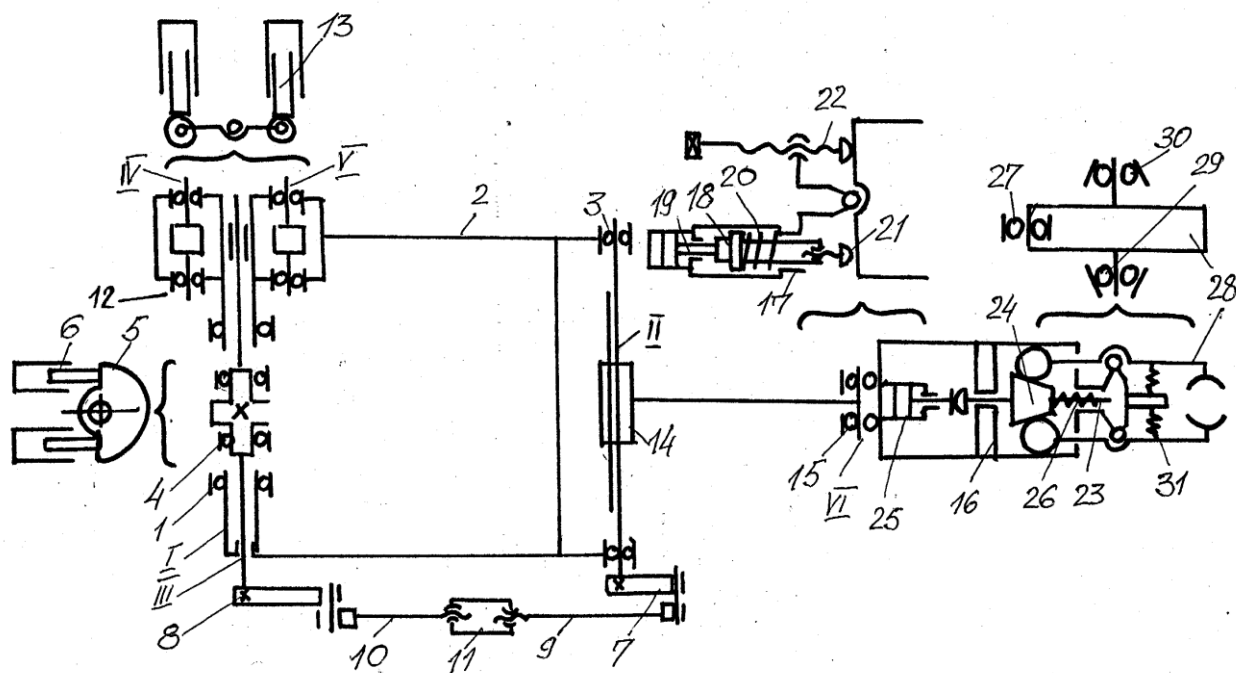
Кинематическая схема манипулятора для съема отливок
